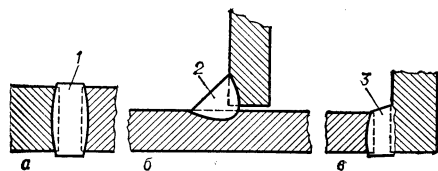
Виды сварных соединений и типы швов при электрошлаковой сварке: а — стыковое; б — тавровое; в — угловое; 1 — стыковой шов; 2 — угловой шов; 3 — шов углового соединения.
